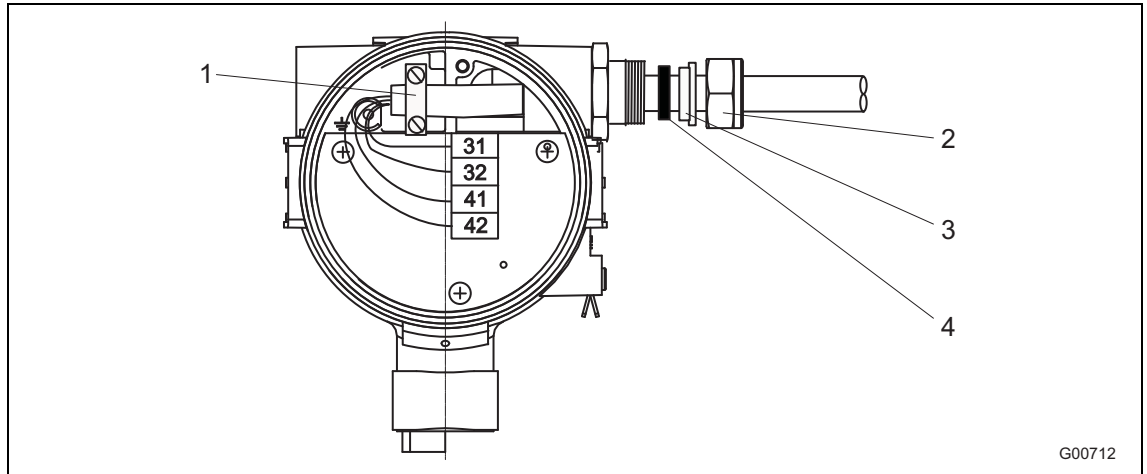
Elektrischer Anschluss der druckfesten Ausführung mit geöffneter Kabelverschraubung
